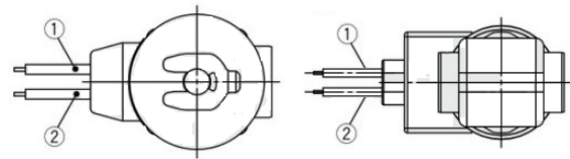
Eingegossenes Kabel und Eingegossenes Kabel mit PCB
